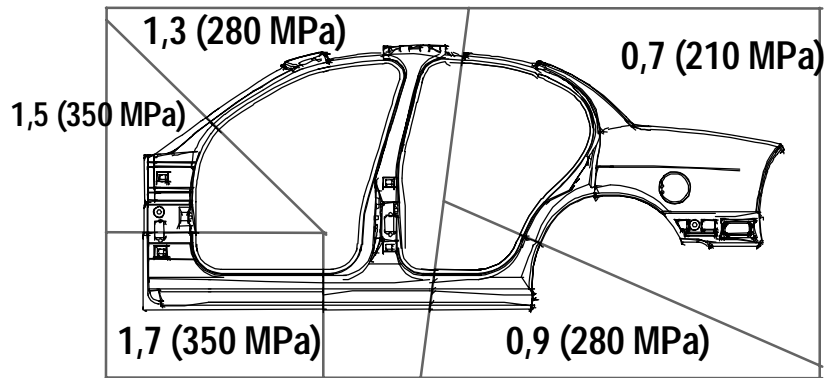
Painel lateral externo. - “*Tailor blank*” soldado a Laser
